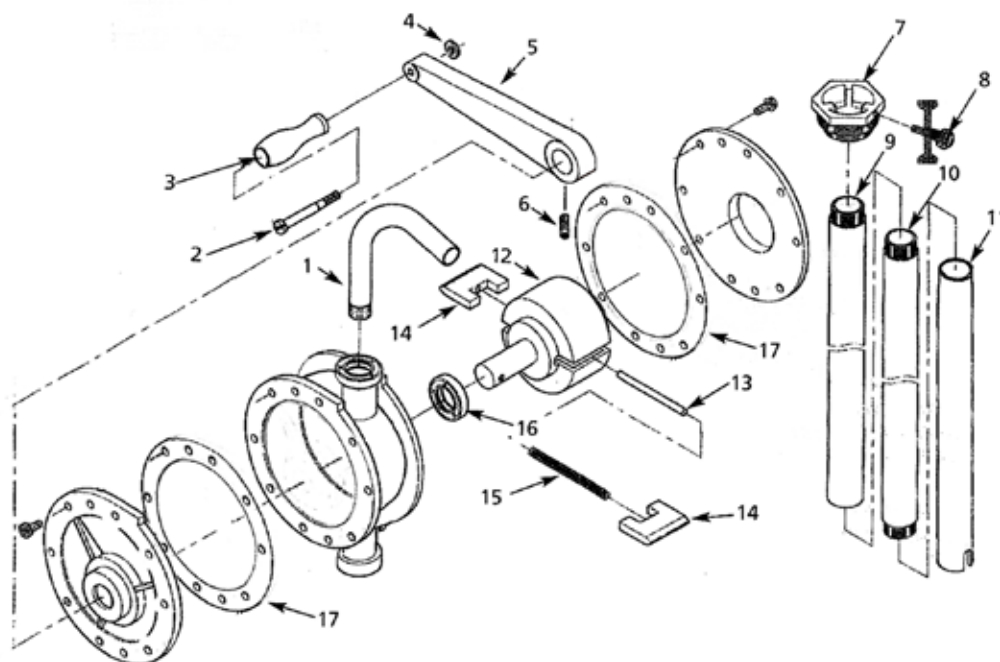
Illustration des pièces de rechange pour pompe Ryton® tambour rotatif
